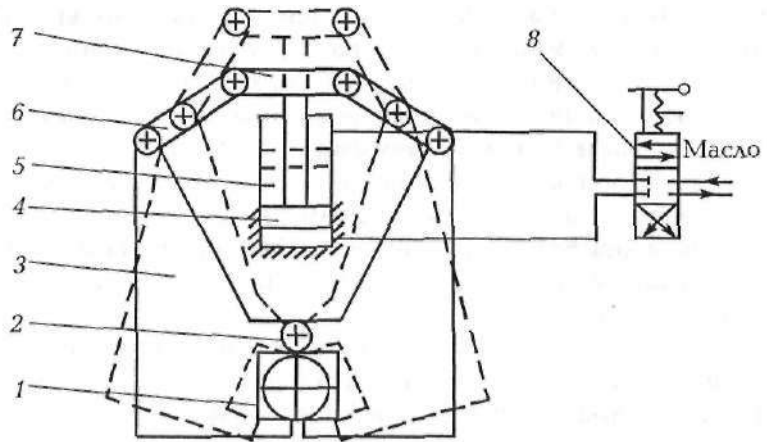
Схема механизма зажатия сварочной машины К-584 М:
